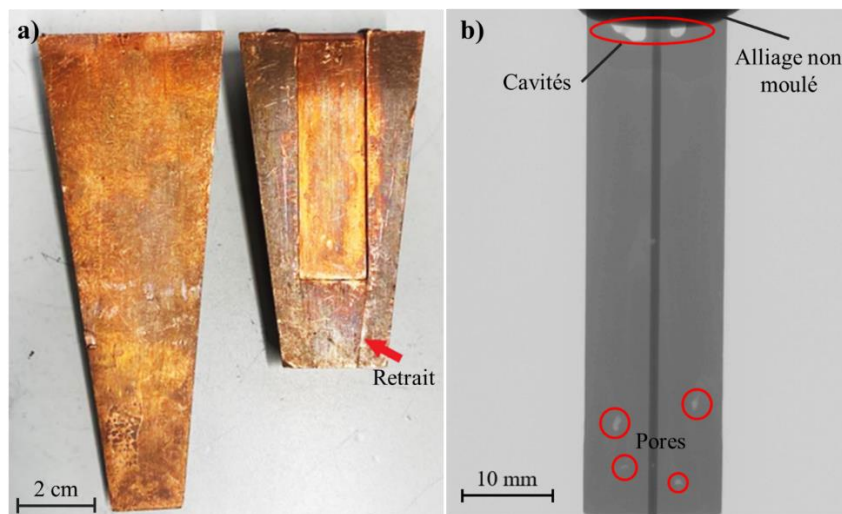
Photographie des moules en cuivre utilisés pour réaliser des plaques d'alliages par fusion par arc - les côtes des plaques sont 50mm*15mm*1mm – la flèche rouge indique un retrait nécessaire pour réaliser la succio (a) ; Radiographie d'une plaque de 1mm de $Mn_{37}Cu_{63}$ réalisée par tomographie aux rayons X. Le trait sombre au milieu s'explique par une surépaisseur du moule à cet endroit (b)
